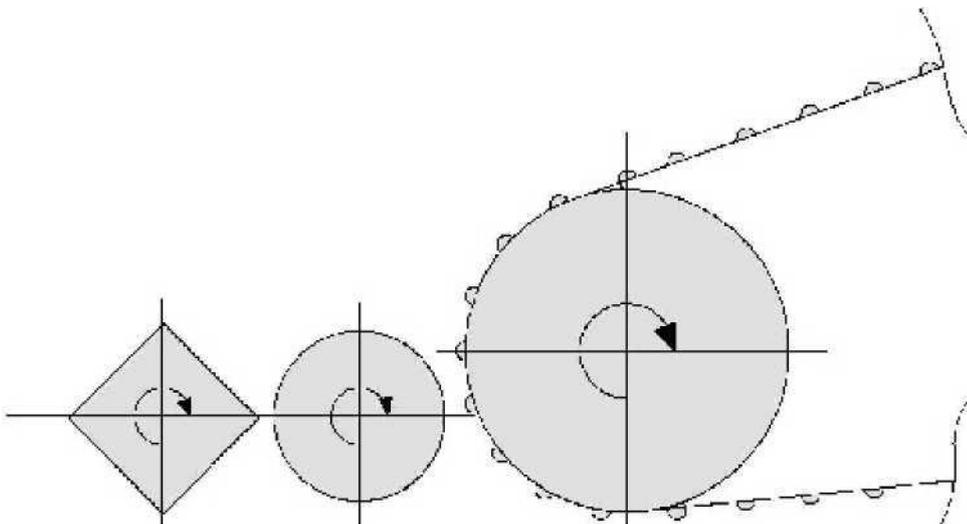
Схема валикового подкапывающего рабочего органа
